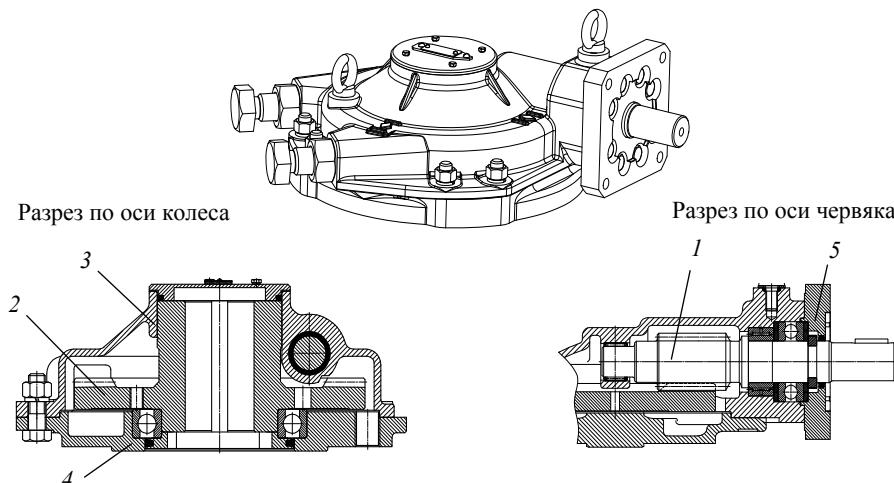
Пример компоновки четвертьоборотного спироидного редуктора ТПА
